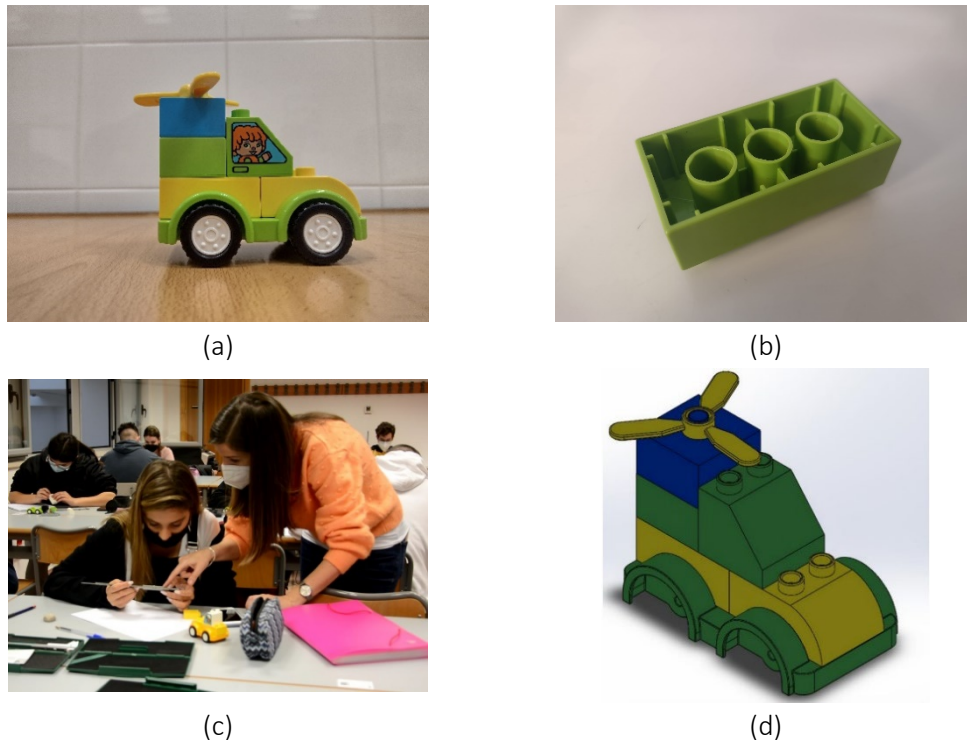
Imagen de uno de los juguetes usados en LEGOFAB (a); detalle de algunas de las piezas del juguete (b); profesora explicando a una alumna el manejo de un pie de rey durante sesiones de metrología (c); conjunto diseñado en 3D mediante el software SolidWorks (d).
